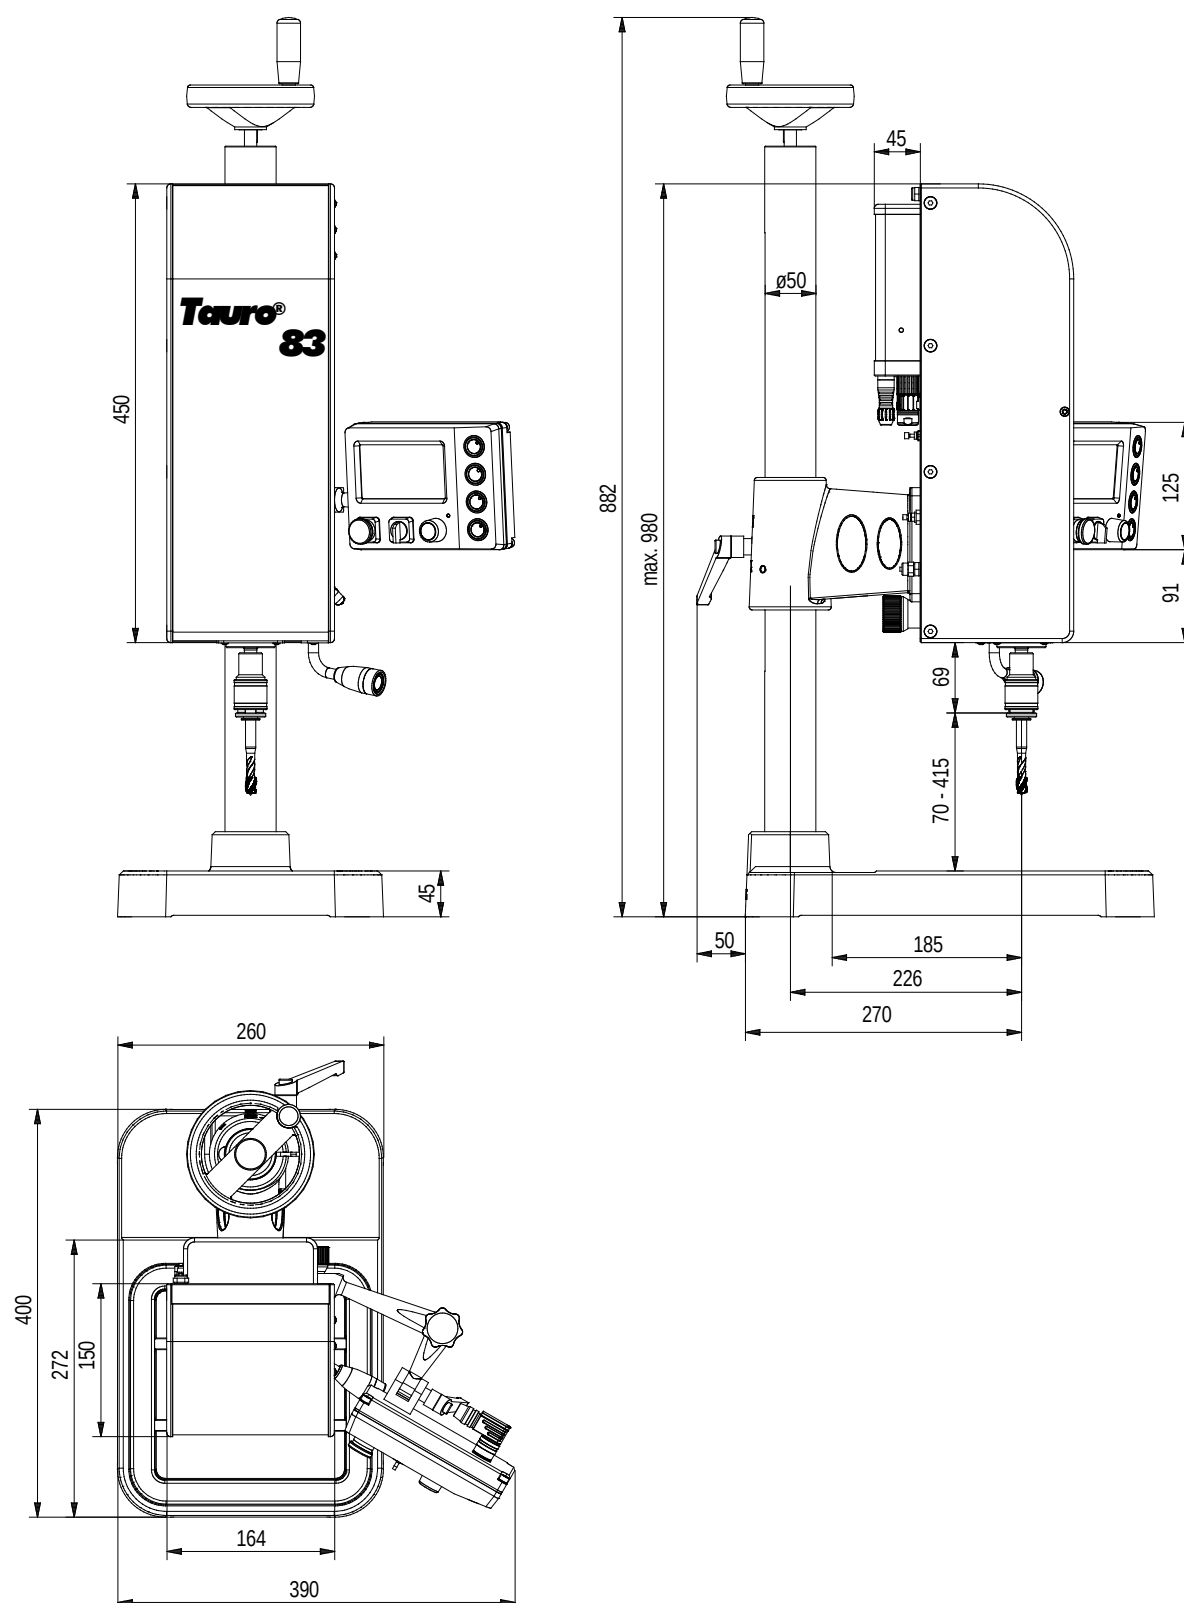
Vues de la machine à usiner les filets Tauro 83
